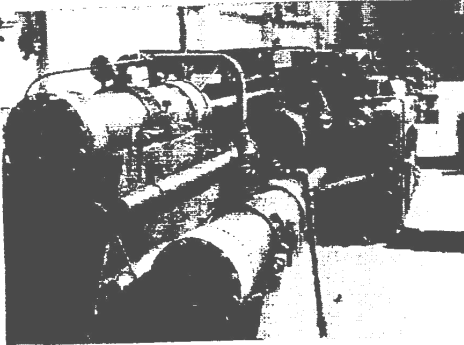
Пневматическое уравнивающее устройство стана ХПТ-55
